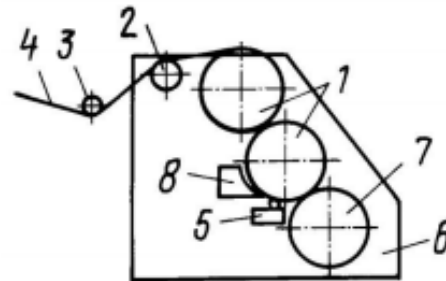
Схема гофропресу: 1 - два гофровала; 2 – зволожувач; 3 – направляючий валик; 4 - полотно паперу, 5 - клейовий пристрій, 6 - станина, 7 - гладкий вал; 8 - напрямна система
